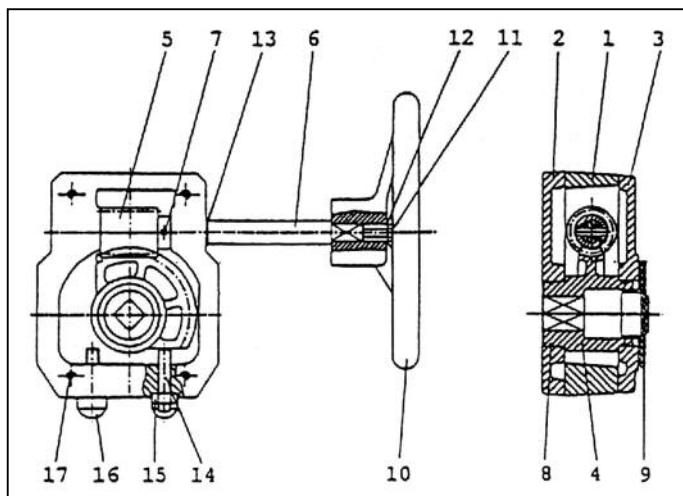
Устройство ручного редукторного привода с червячной передачей.
